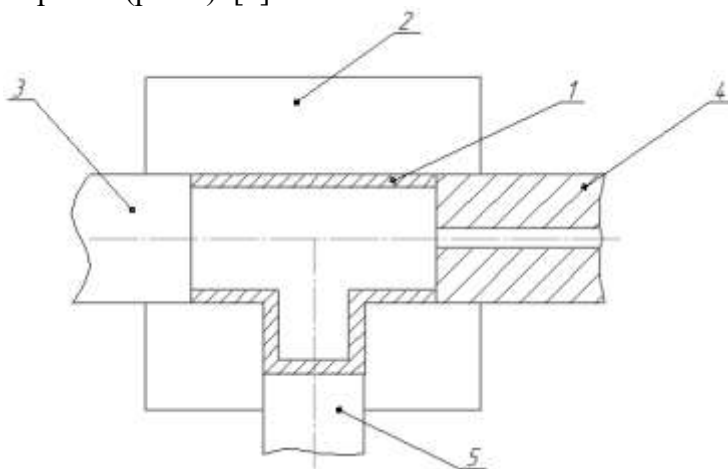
Схема процесса гидроштамповки тройника из трубной заготовки: 1 — тройник; 2 — разъемная матрица; 3, 4 — осевые пуансоны; 5 - пуансон противодействия (подпора)
